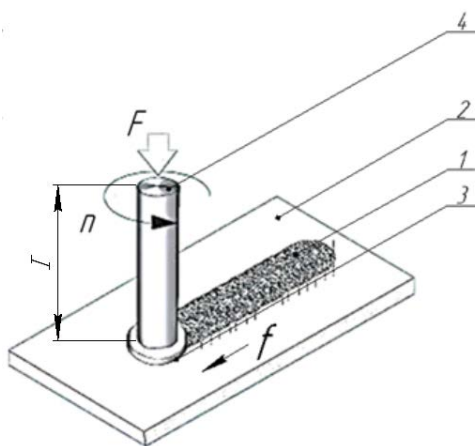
Схема процесса фрикционного нанесения. Цифрами обозначены: 1 - нанесенный слой; 2 – подложка; 3 – расплавленный упрочняющий материал; 4 – стержневая заготовка.
